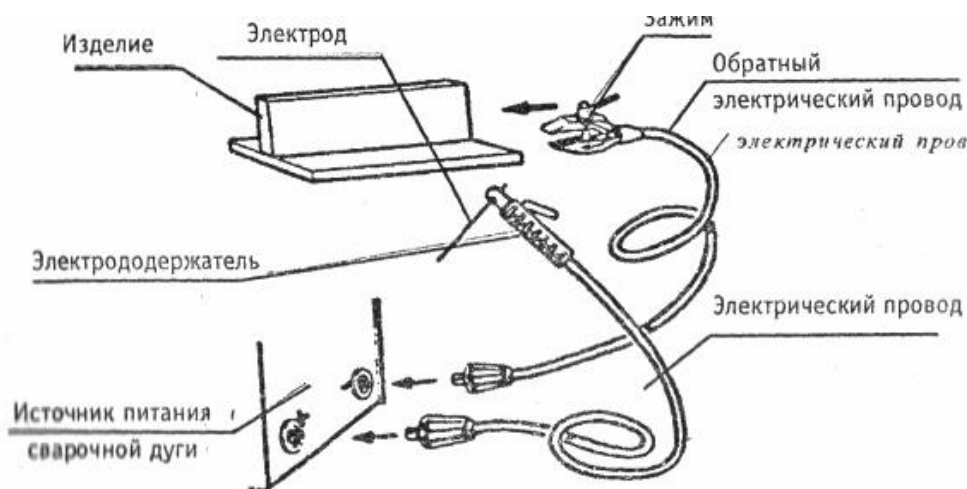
Схема подключения сварочного оборудования
